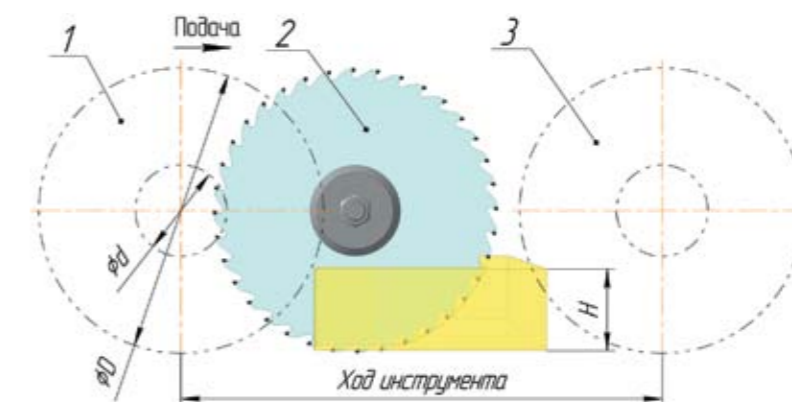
Рабочий цикл (горизонтальная подача) положения торцовочной пилы: 1 – исходное; 2 – промежуточное; 3 – конечное
